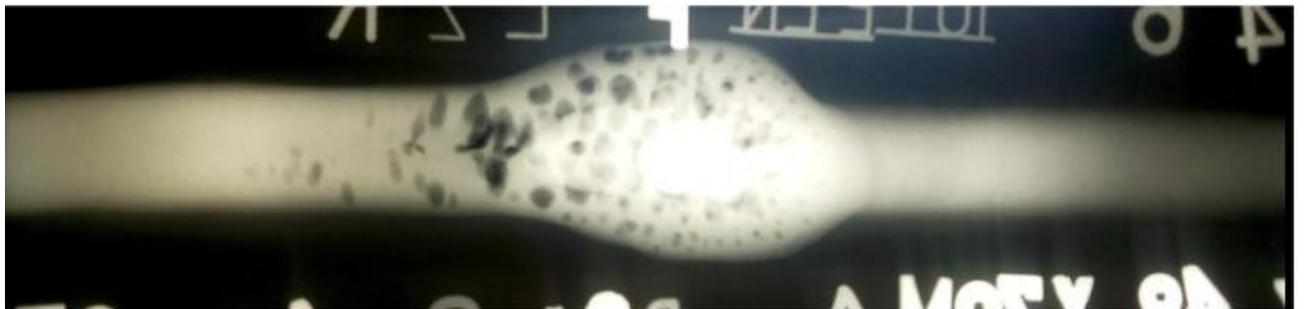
ILLUSTRATION D'UN DEFAUT D'INCLUSION DANS UN CORDON DE SOUDURE.
